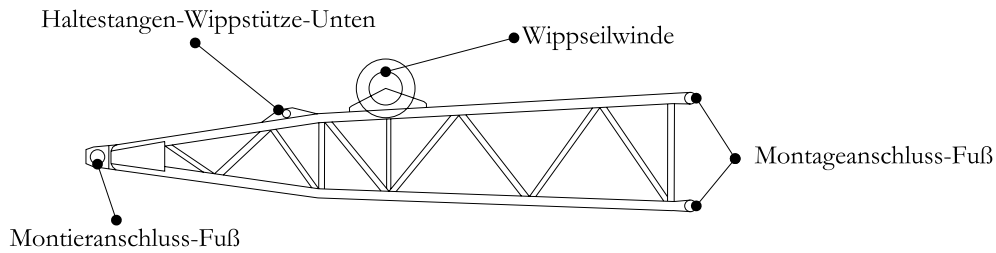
Anschlüsse des Bauteilprototypen Fußstück
